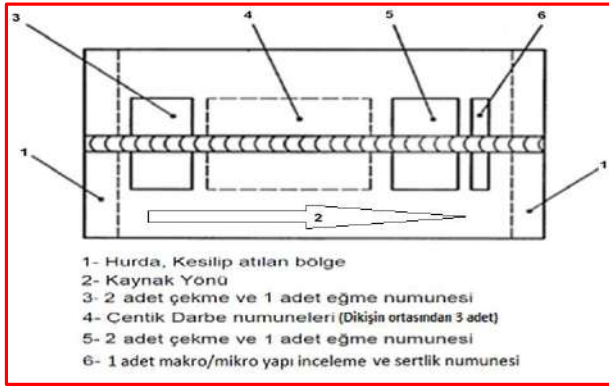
Kaynak işlemi için hazırlanan test parçaları (Test parts prepared for welding process)
